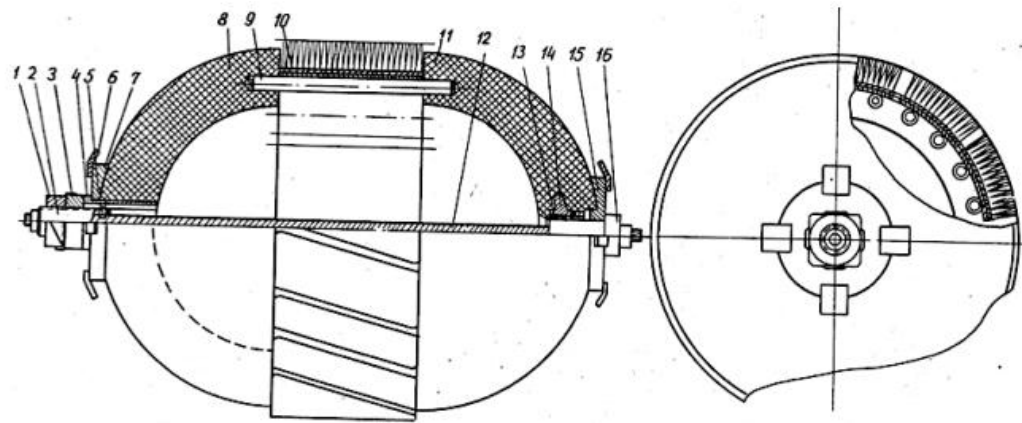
Общий вид шарового резинового скребка с металлическими щетками
